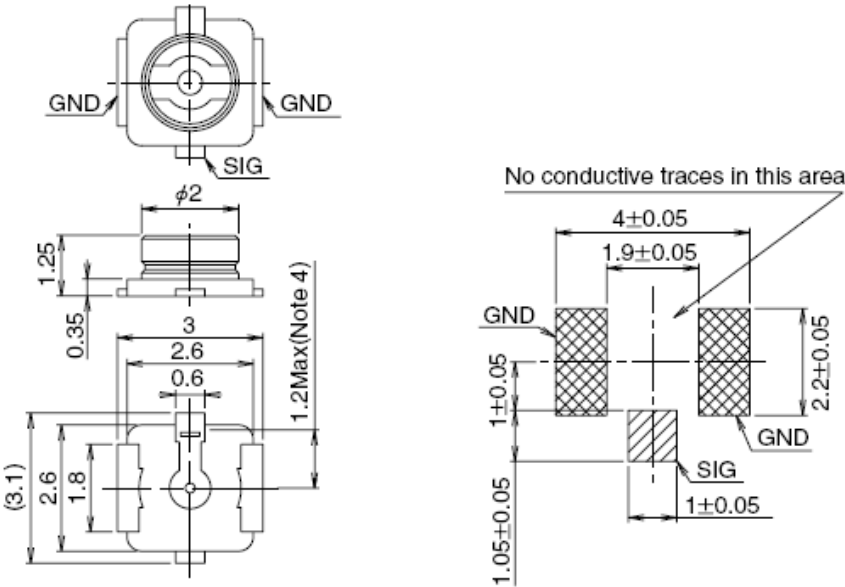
U.FL-R-SMT 连接器尺寸 (单位: 毫米)
